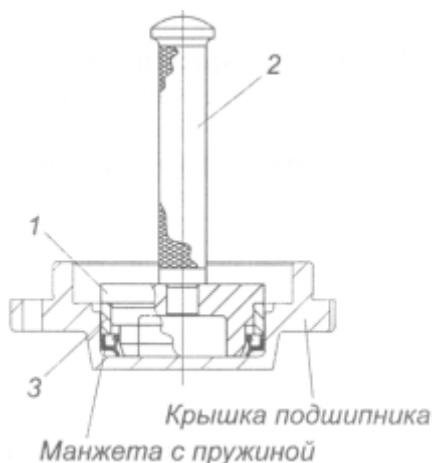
Запрессовка манжеты ведущей шестерни: 1 - Оправка ОЗМ 10.001; 2 - Ручка ОЗНК 42206.00.002; 3 - Втулка ОЗМ00.003.
